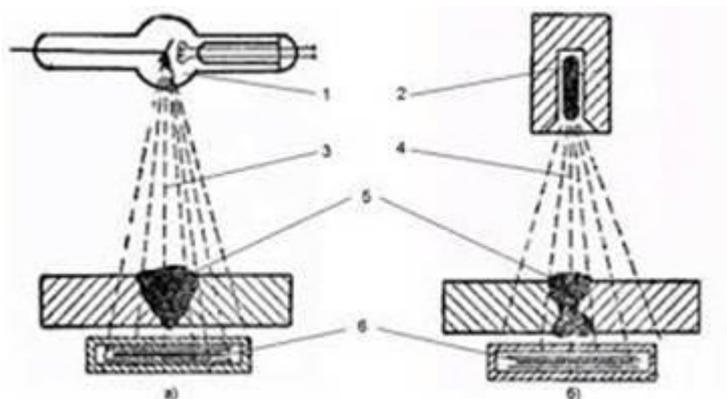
Схема просвечивания сварных швов рентгеновскими лучами
